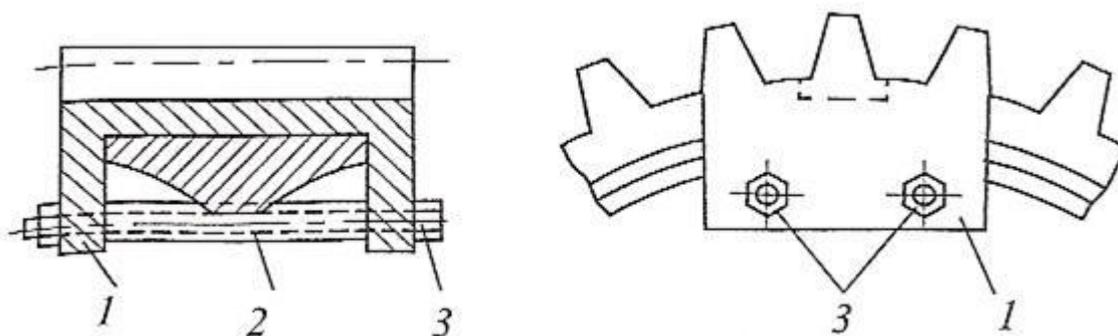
Схема ремонта зубчатого колеса при помощи башмака: 1 - башмак; 2— распорная втулка; 3— болт
